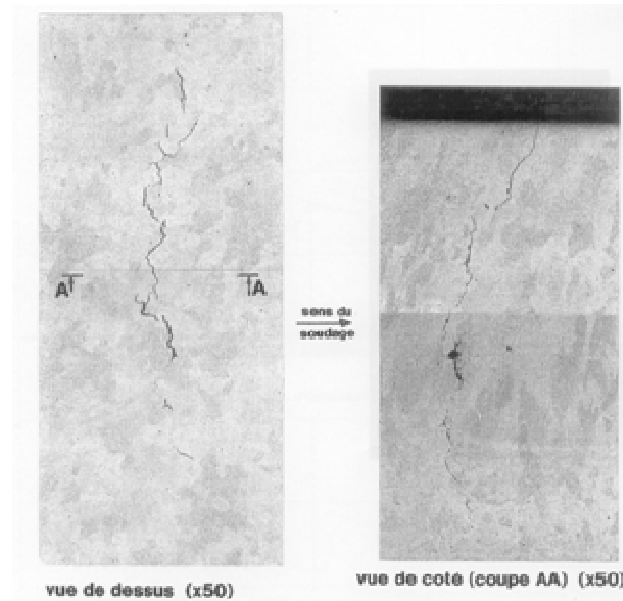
Fissuration transversale d'une soudure multipasses
